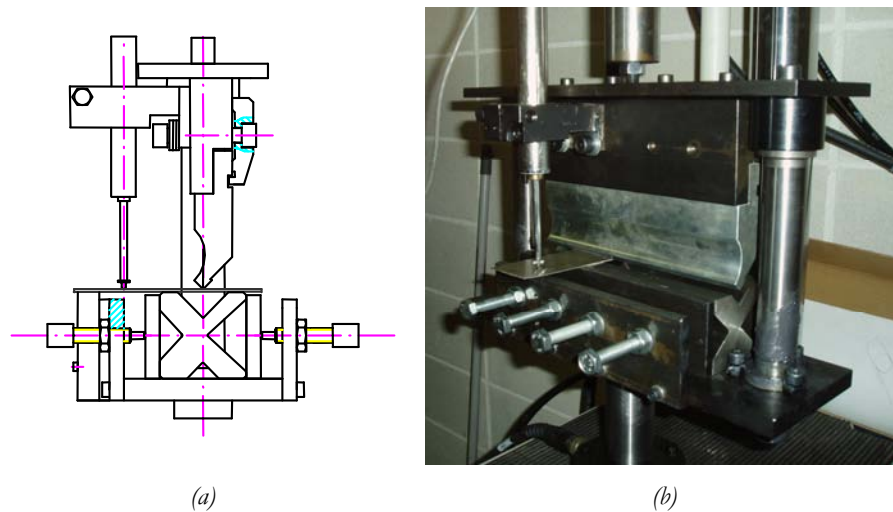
Utillaje de medición del ángulo en carga definitivo (a) Diseño del montaje final con chapa plana (b) Montaje real llevado a cabo sobre chapa doblada en carga
